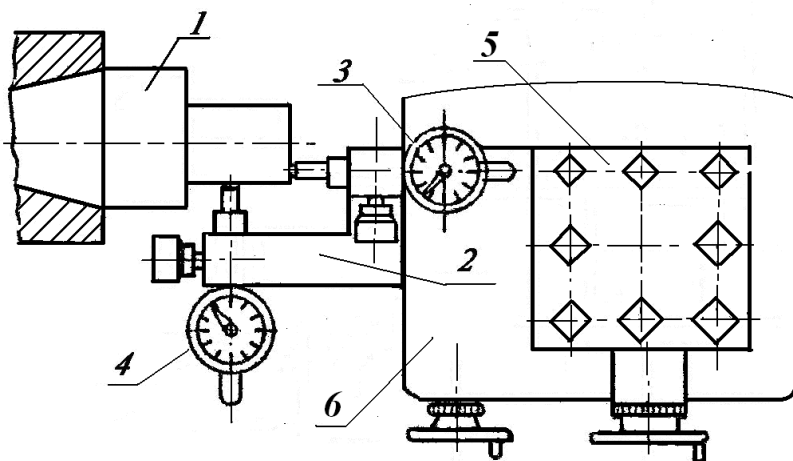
Схема измерения отклонений размеров статической настройки по лимбам токарного станка :1 – упор специальный, 2-державка индикаторная, 3,4 – индикаторы часового типа, 5 – резцедержка, 6 – суппорт
